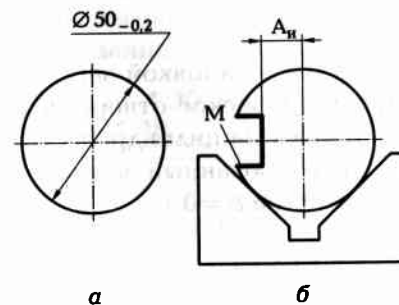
Схема установки заготовки (a) на призму при фрезеровании ($б$) паза
